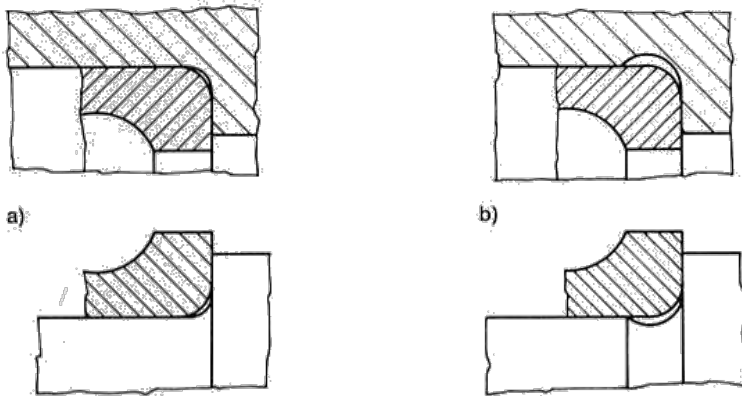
Il passaggio dalla sede cilindrica allo spallamento può avvenire: a) mediante raccordo; b) mediante gola di scarico. In entrambi i casi il raccordo deve consentire l'appoggio degli anelli agli spallamenti.
